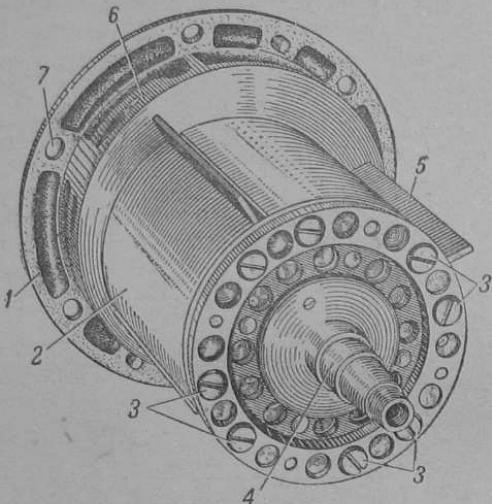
Ротор нагнетателя двигателя С2Б в сборе:
